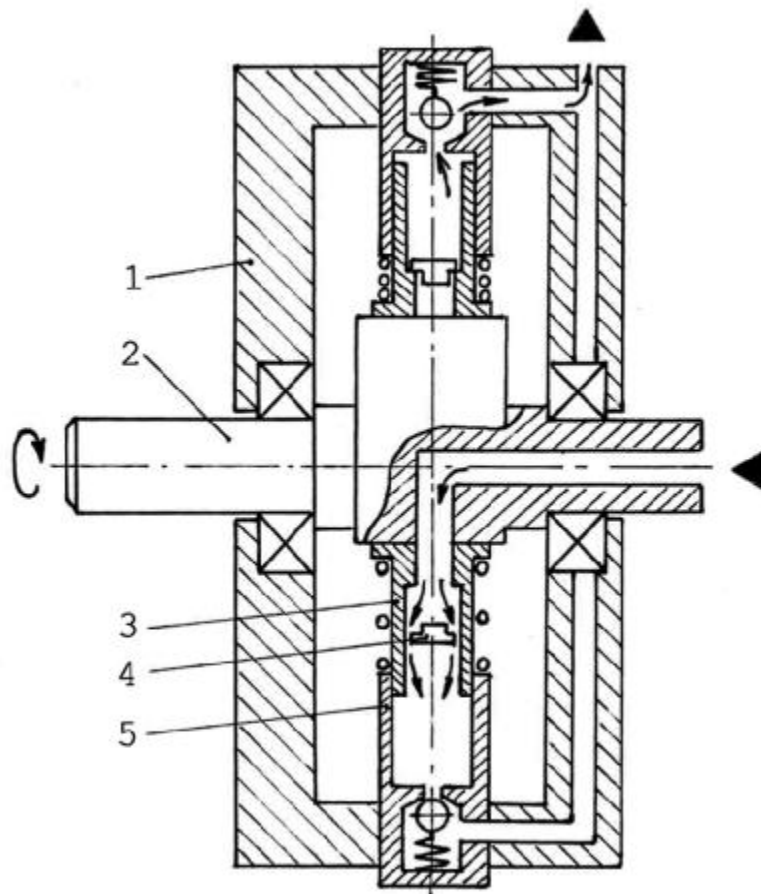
Кинематическая схема радиально – поршневого насоса: 1 – корпус; 2 – вал с эксцентриком; 3 – поршень; 4 – всасывающий клапан; 5 – цилиндр.
